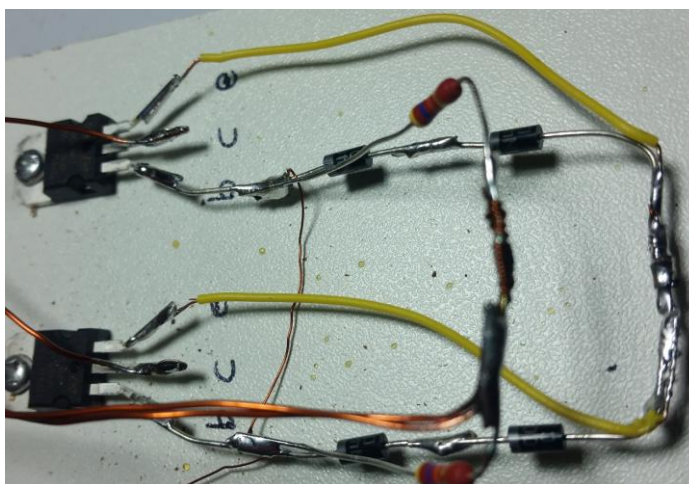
Resistores soldados e ligados à bobina.
